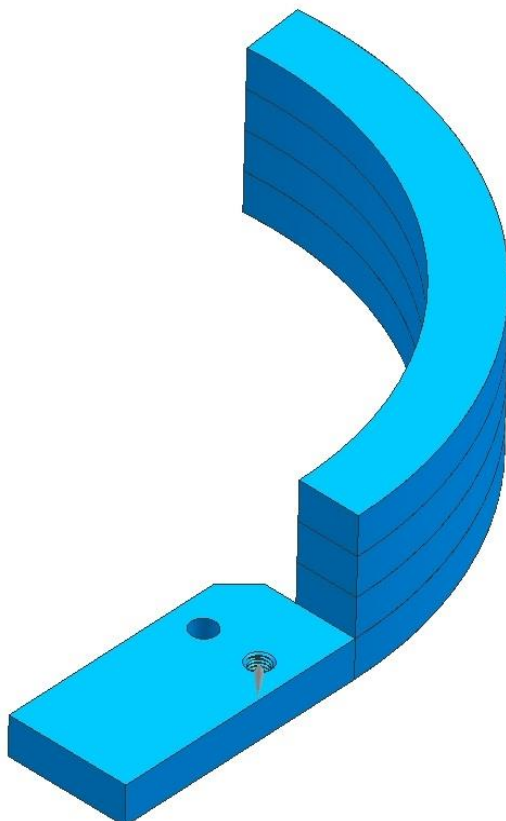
Horní díl, varianta č. 4 – půdorys (vpravo)
